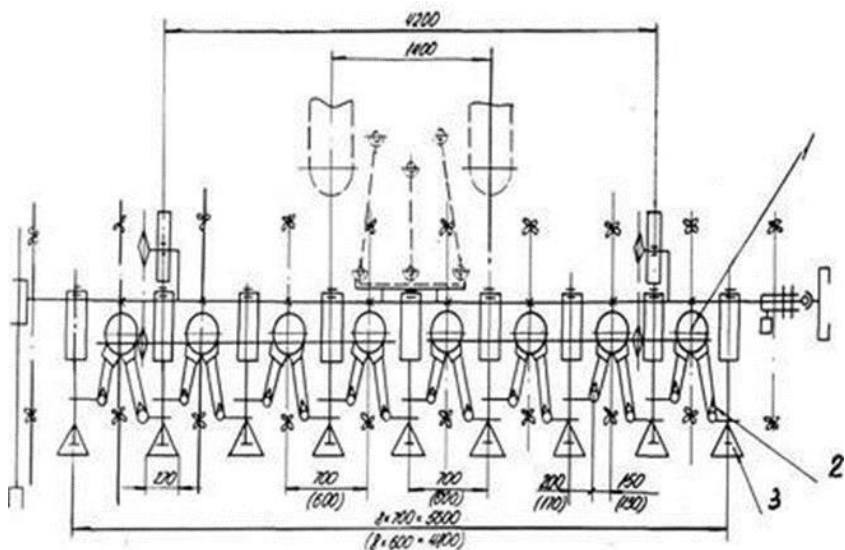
Схема расположения рабочих органов культиватора КОР-4 с подкормочным приспособлением (ширина междурядий 60, 70 см): 1 - аппарат туковывсевающий; 2 - раструб ножа; 3 - лапа (захват 270 мм)
